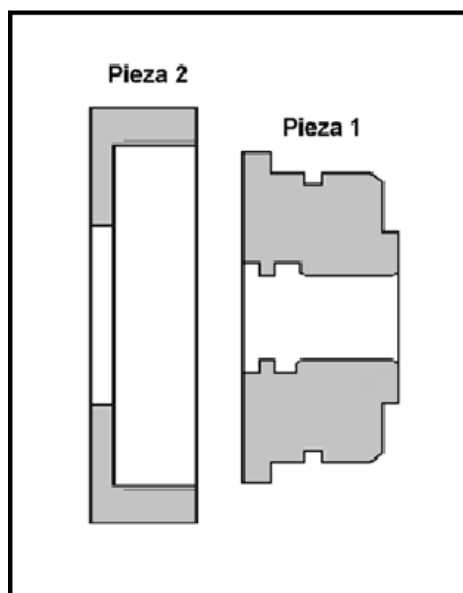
PARTES DE TAPA DE CILINDRO
